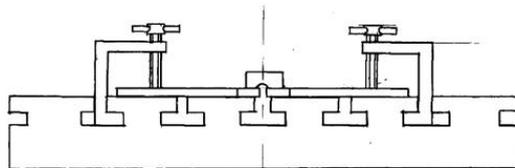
Схема сборки поперечного сварного шва карты
